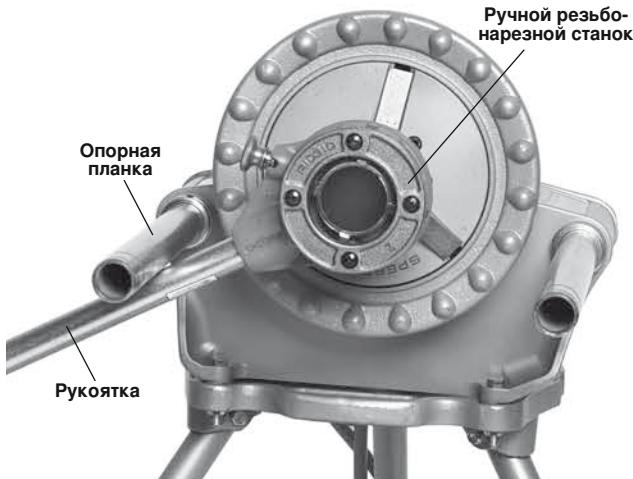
Снятие резьбонарезной головки с резьбовой трубы (рукоятка упирается в нижнюю часть стержня).
